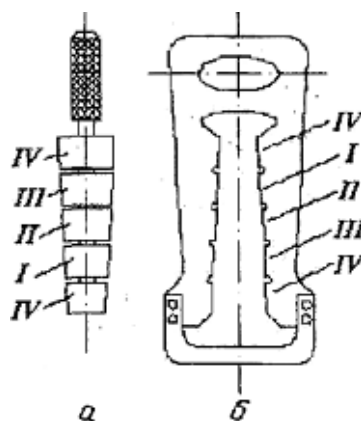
Схемы калибров для сортирования деталей: *а и б* - ступенчатые пробка и скоба; /... III - рабочие размерные группы; IV- размерная группа брака
